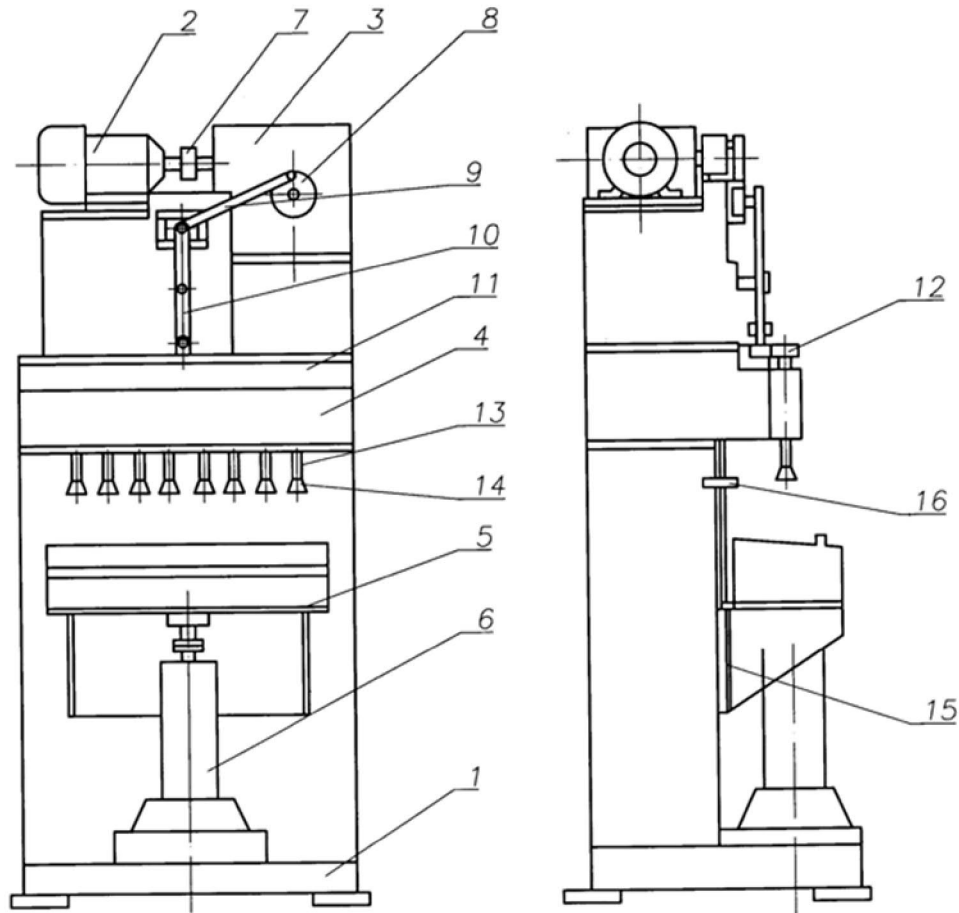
Стенд для притирки клапанов двигателя автомобилей
